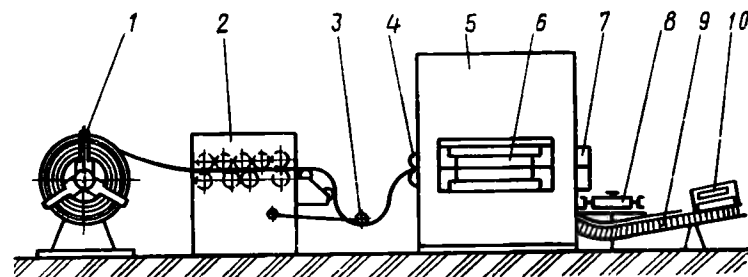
Схема штамповки на автоматической штамповочной установке:
